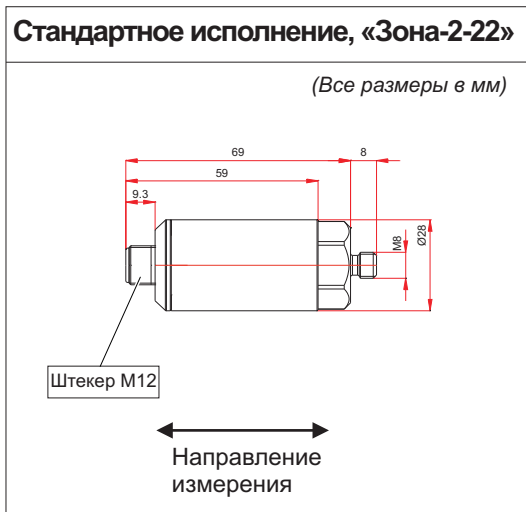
Размеры корпуса и направление измерения: стандартное исполнение, «Зона-2-22».
